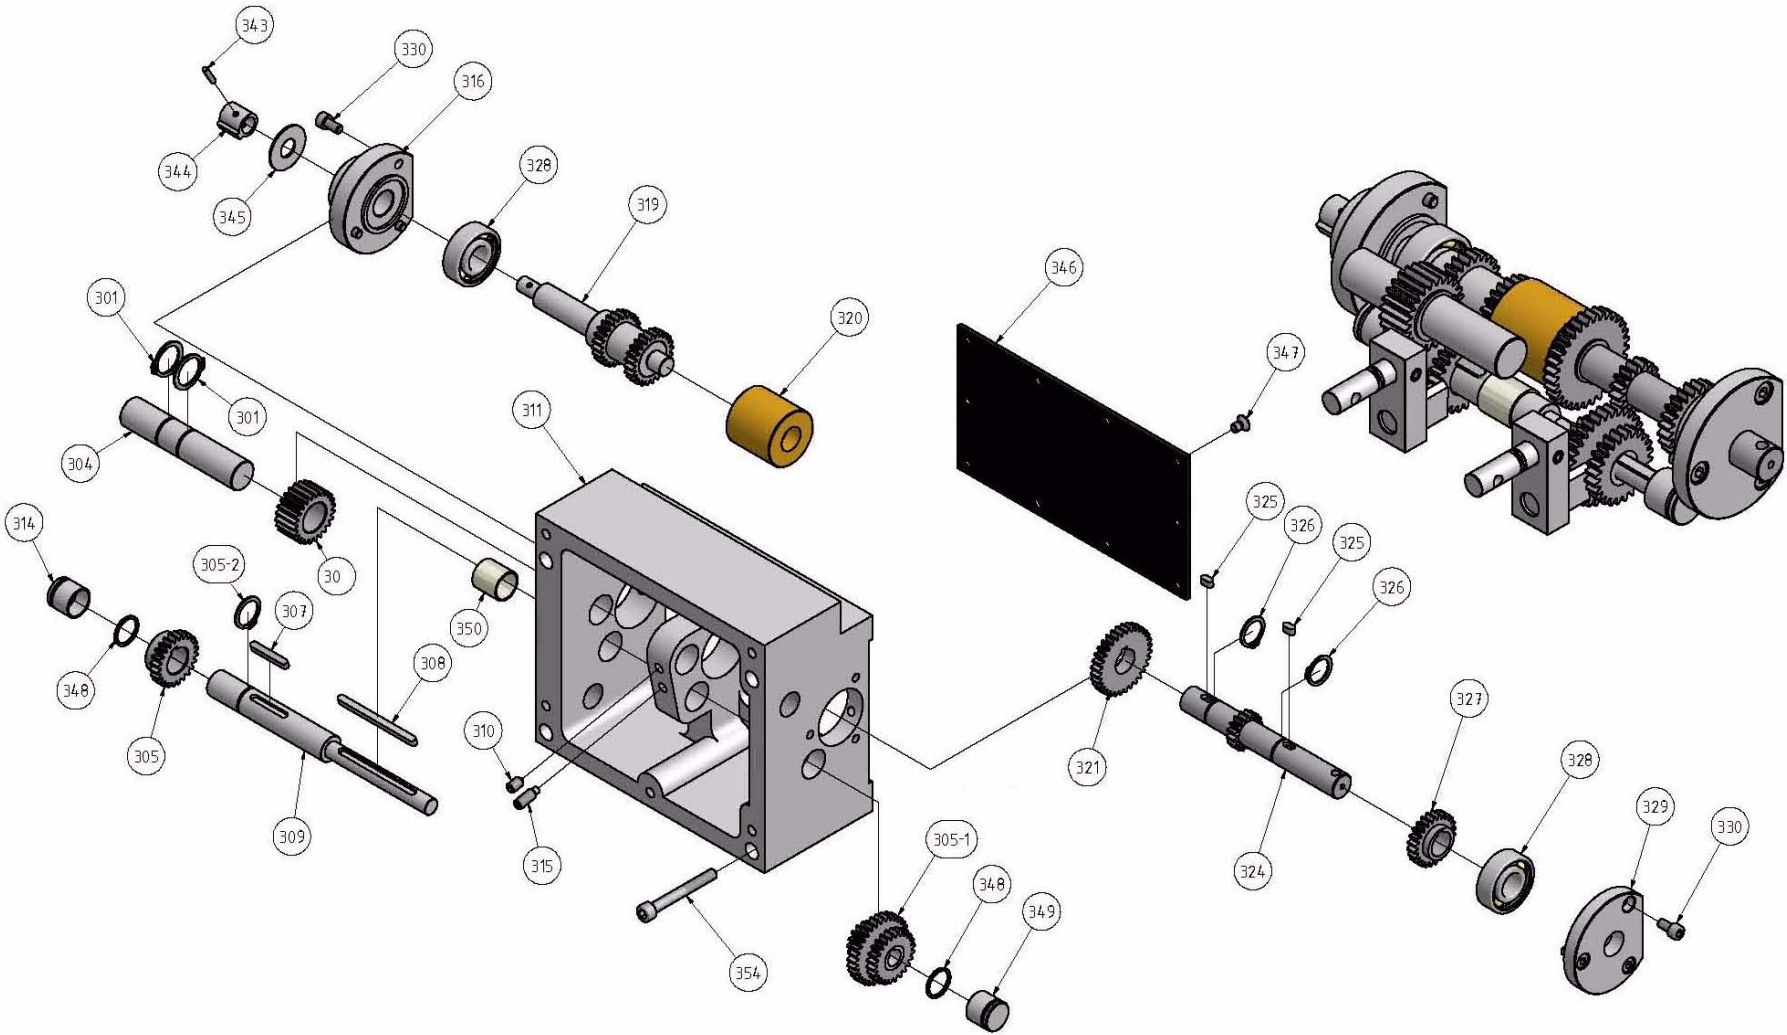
Vorschubgetriebe D280 2 von 2 - Feed gear D280 2 of 2
